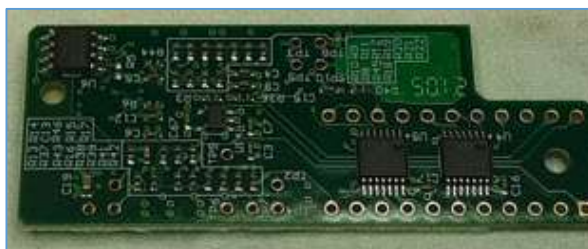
Interface électronique à intégrer sur la carte graphique du VNA ; vue du côté soudures. Photo : ON4IJ.
